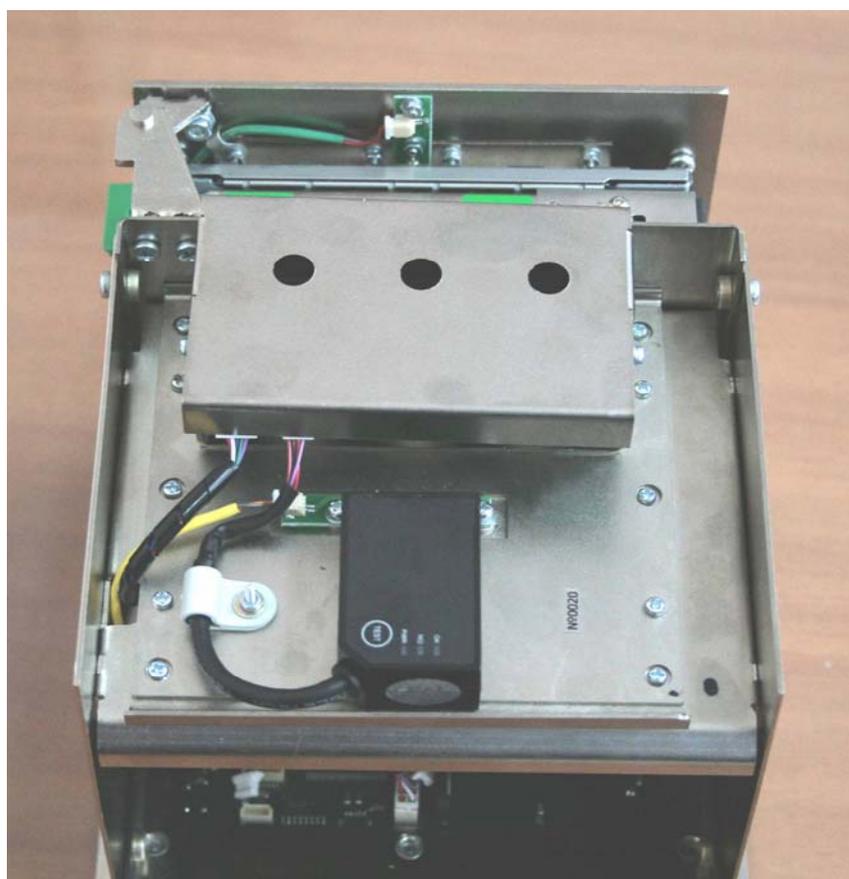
Внешний вид блока печати (вид сверху)
